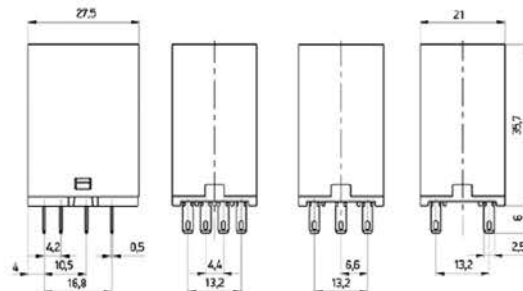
Габаритные, установочные, присоединительные размеры реле OptiRel G RP55-3X
